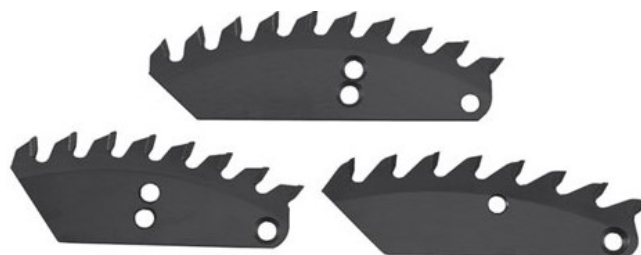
Příklady využití svařování a navařování [2], [3], [4], [6]
